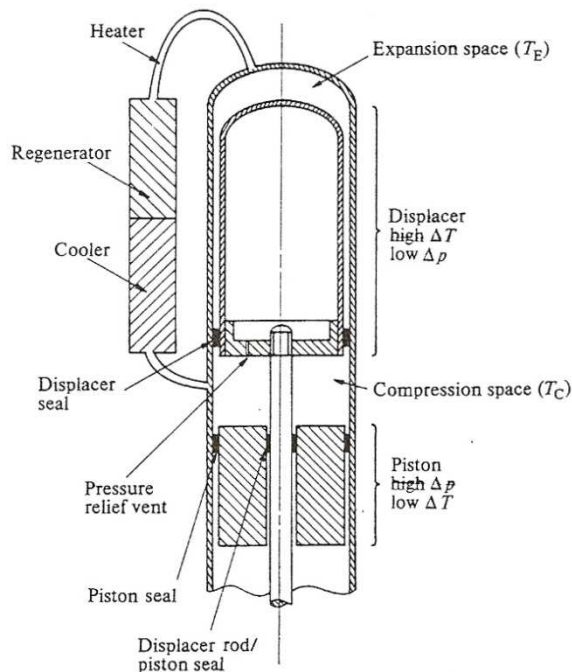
Macchina di Stirling monocilindrica (beta)
